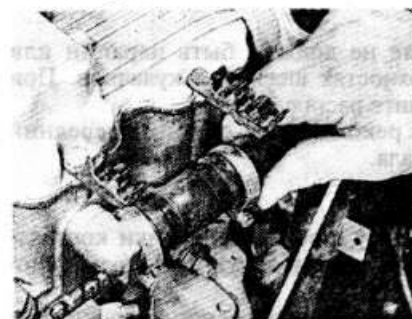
Отсоединение шланга сапуна картера двигателя от кожуха распределительного вала — двигатель типа SOHC с рабочим объемом 2,0 л
